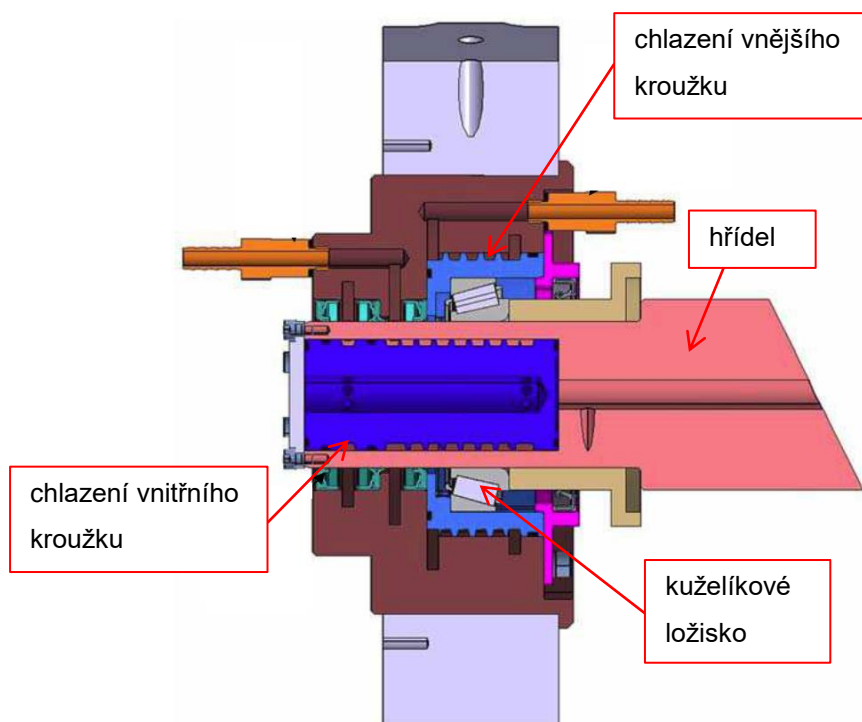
Testovací stand vytvořený Ing. Mackem [7]
